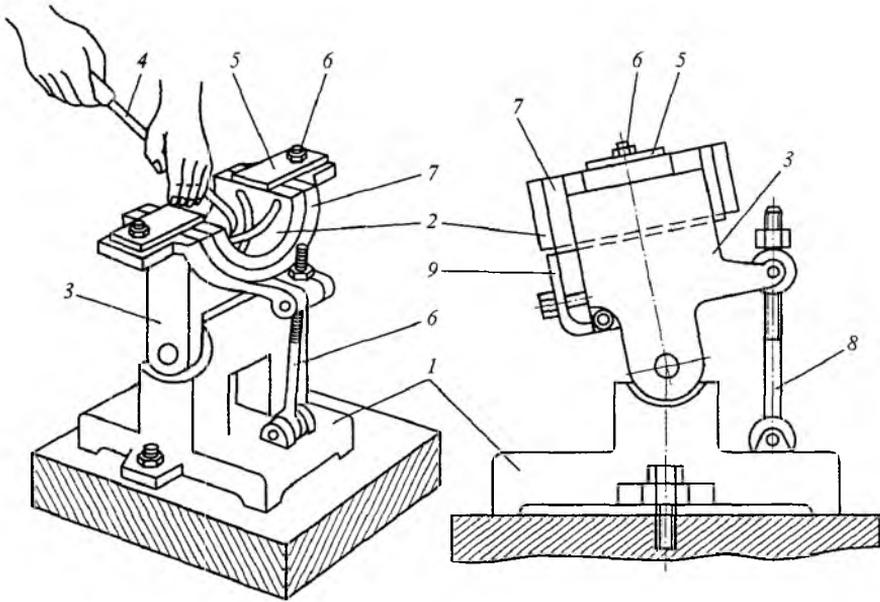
Приспособление для шабрения вкладышей подшипника скольжения: 1 – основание; 2 – вкладыш; 3 – стойка; 4 – шабер; 5 – планка; 6, 8 – винты; 7 – полукольцо; 9 – прижим
